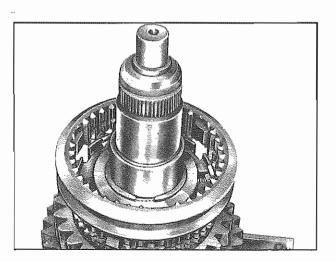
Montaggio del manicotto sincronizzatore Fitting the syncromesh sleeve
